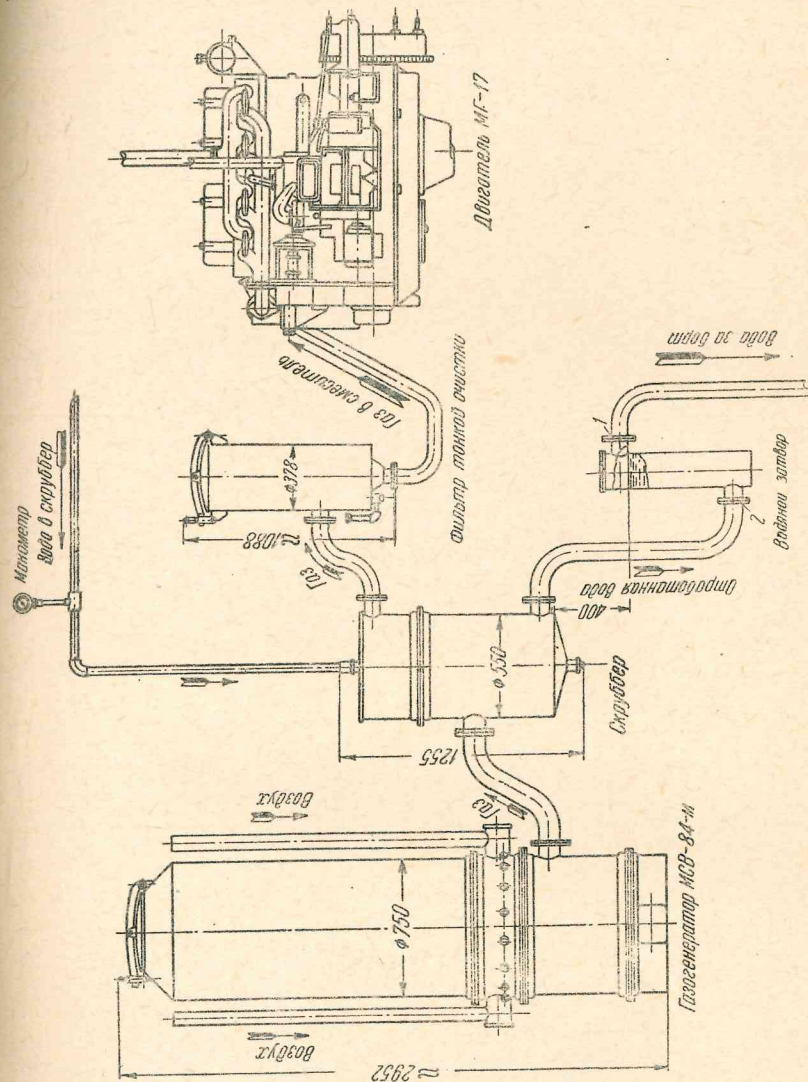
Принципиальная схема газогенераторной установки под двигатель МГ-17
